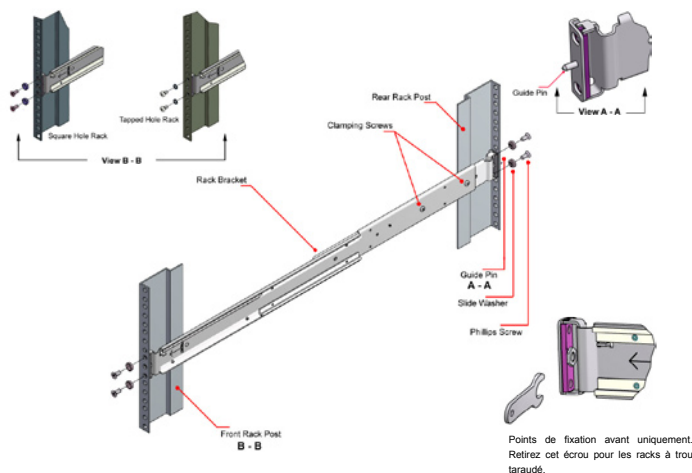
fixation des supports au rack (ensemble gauche illustré)
